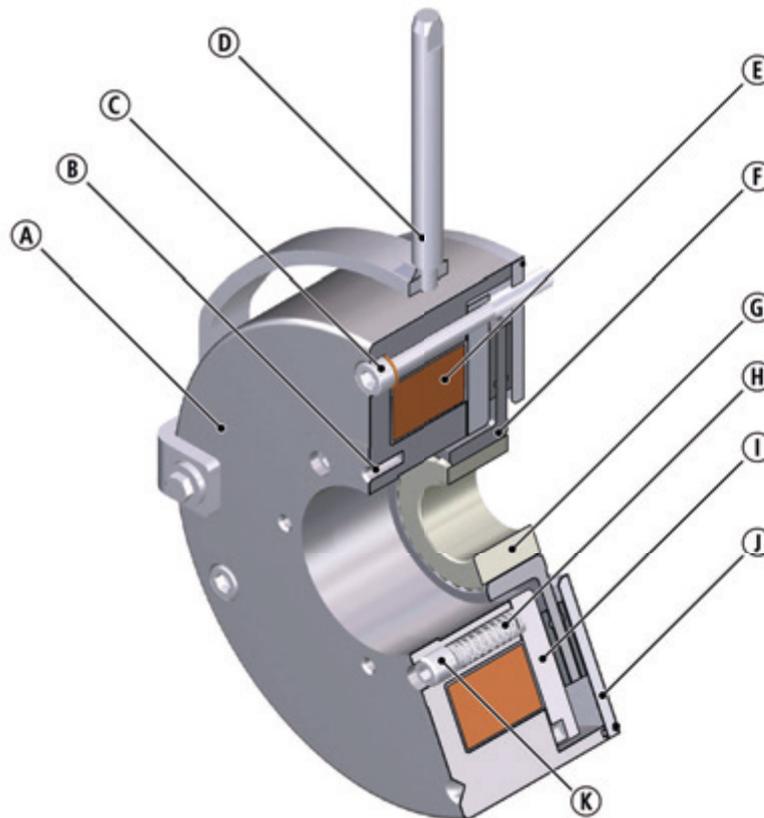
Aufbau einer Federkraftbremse INTORQ BFK470: Magnetteil komplett + Rotor + Flansch
